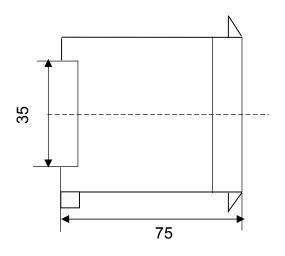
Габаритные и установочные размеры ИП в корпусе 110x120x70 mm с креплением на DIN – рейку (35 mm)
